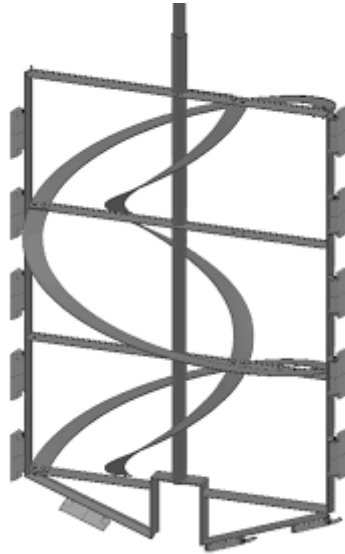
Przykłady konstrukcji mieszadeł kratowych [31, 96]
